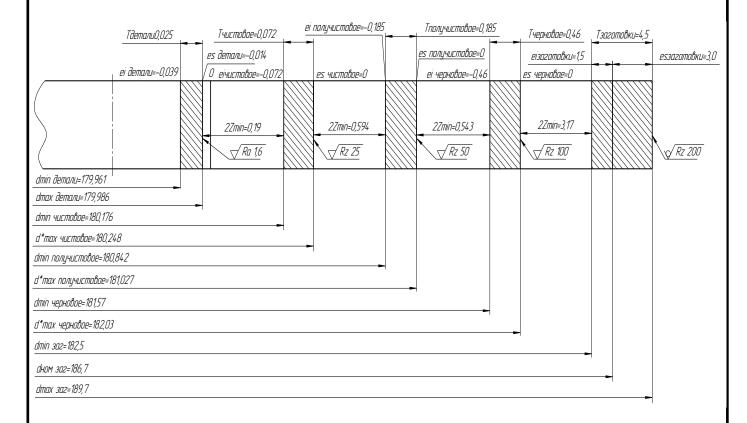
Схема расположения припусков и допусков для наружной цилиндрической поверхности Ø180g6(-0,014;-0,039)
